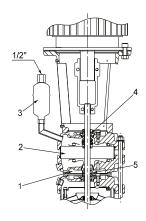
CR 32, 45, 64 und 90 mit luftgekühlter Wellendichtungskammer
